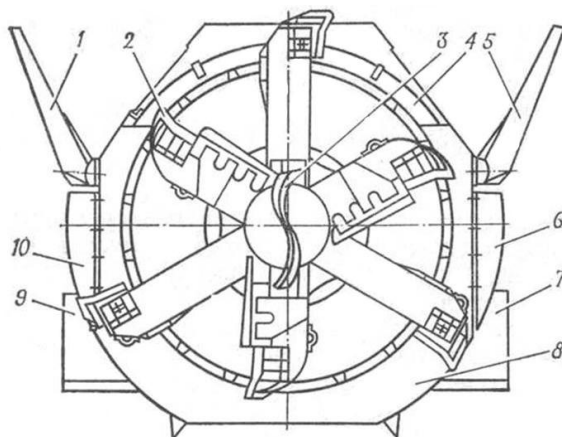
Робочий орган (вид ззаду): 1 і 5 – укосини; 2 – фреза; 3 – забурювач; 4 –
